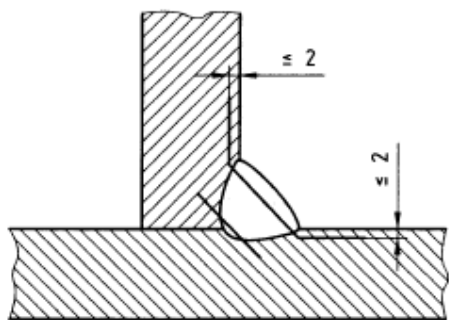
钢材焊缝行检验 (R) 示意图 (mm)
